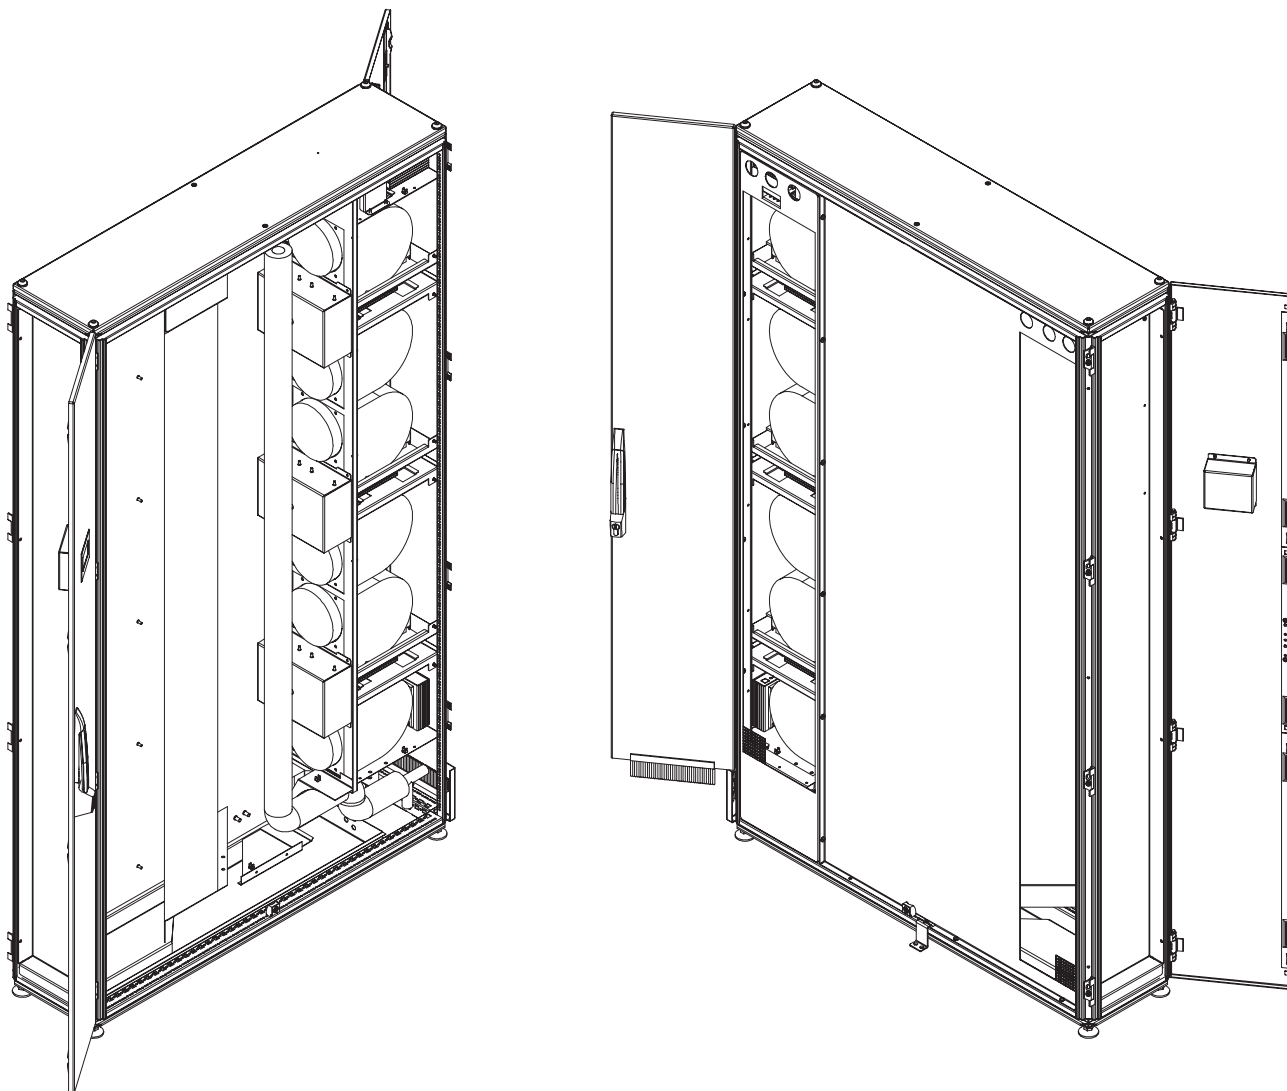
Обзорный чертеж – Liquid Cooling Package Plus EC (изометрия)
